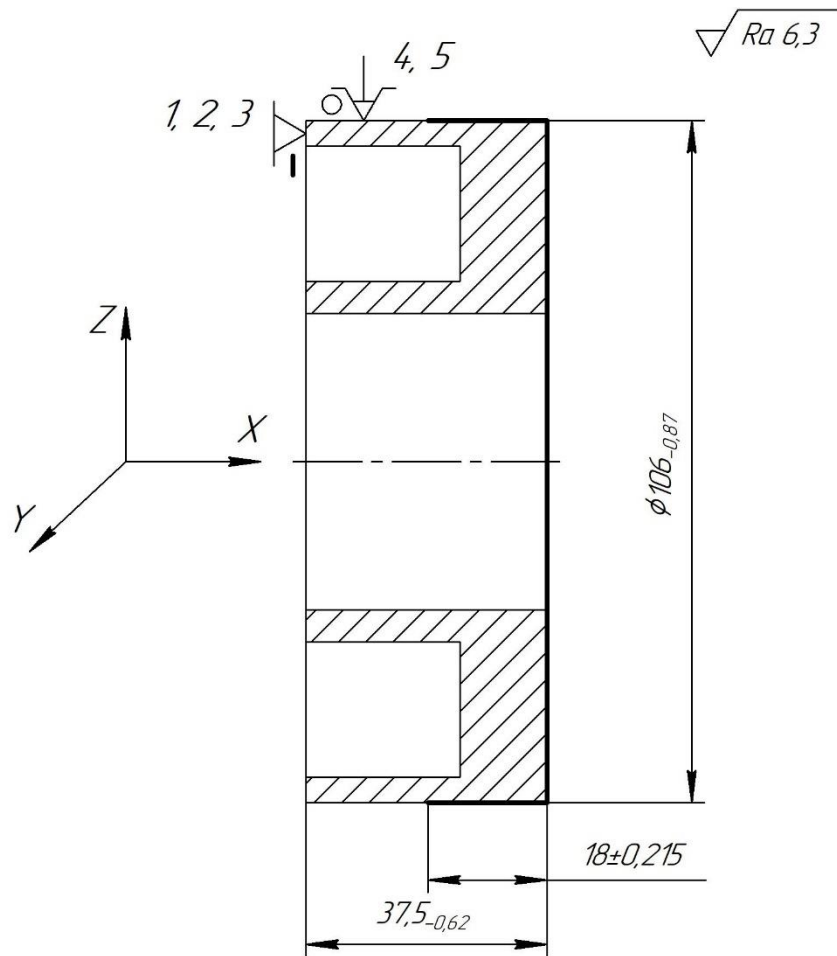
Схема базування й закріплення заготовки на операції 025, установ Б
